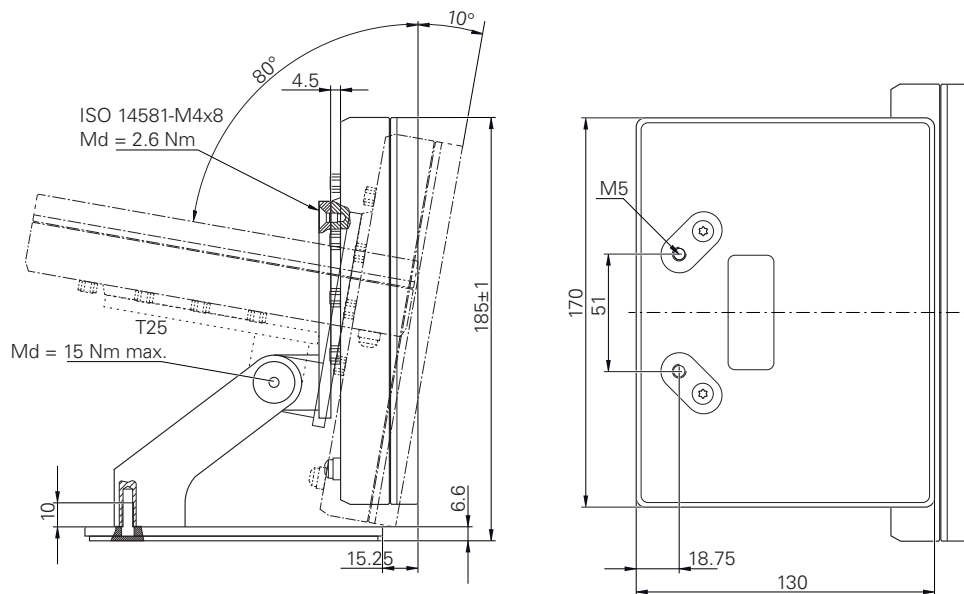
Dimensiones del aparato con pie de soporte Multi-Pos
